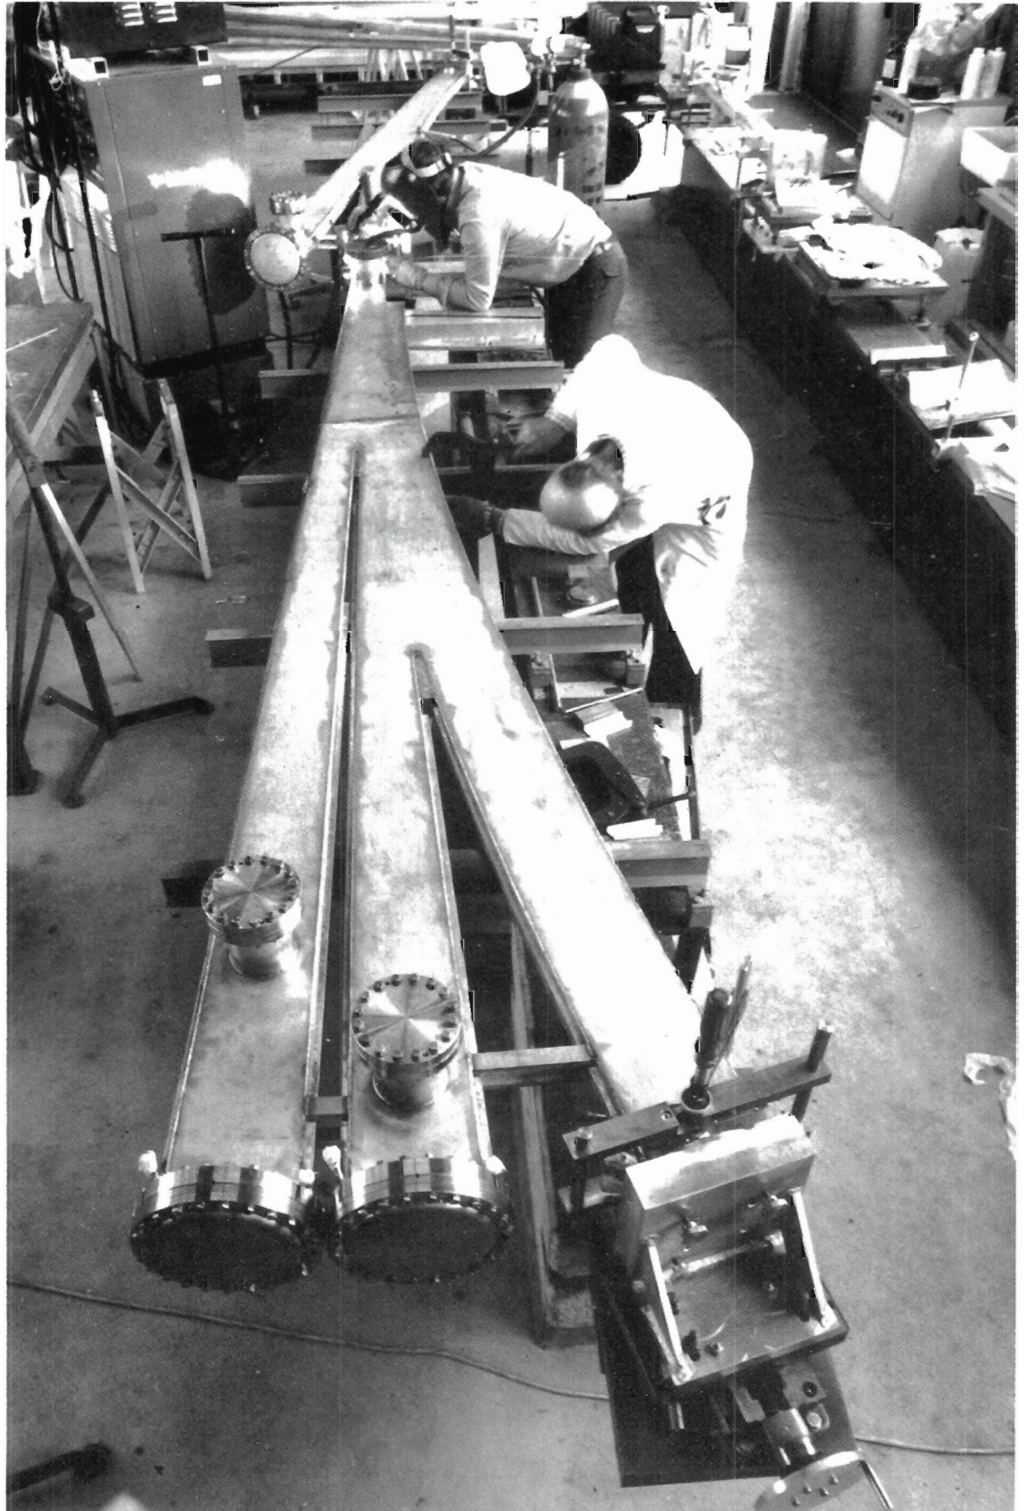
Zusammenschweißen einer Doppelauslaß-Vakuumkammer für DORIS II.
